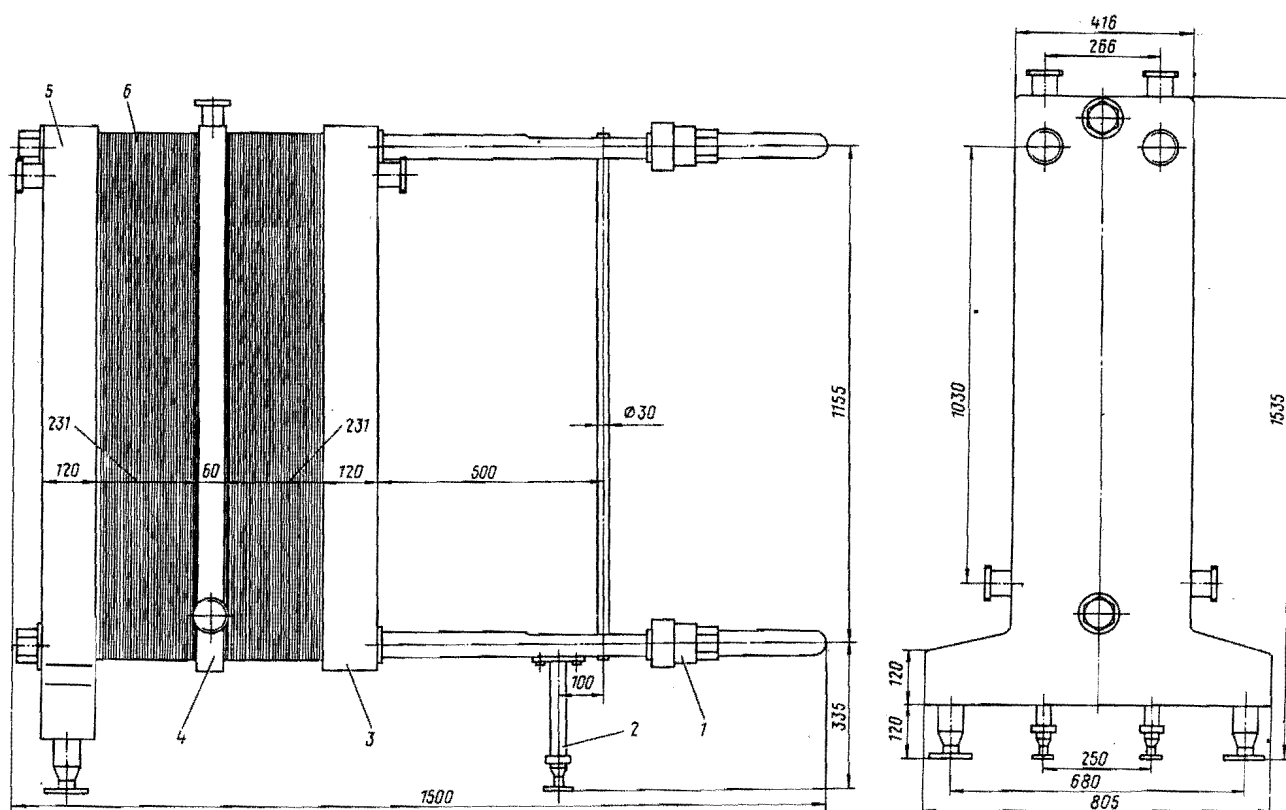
Общий вид установки пластинчатой марки А1-ОКН для охлаждения кефира:
